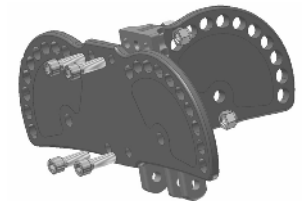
Befestigung einer Halbplatte an Hauptplatte
